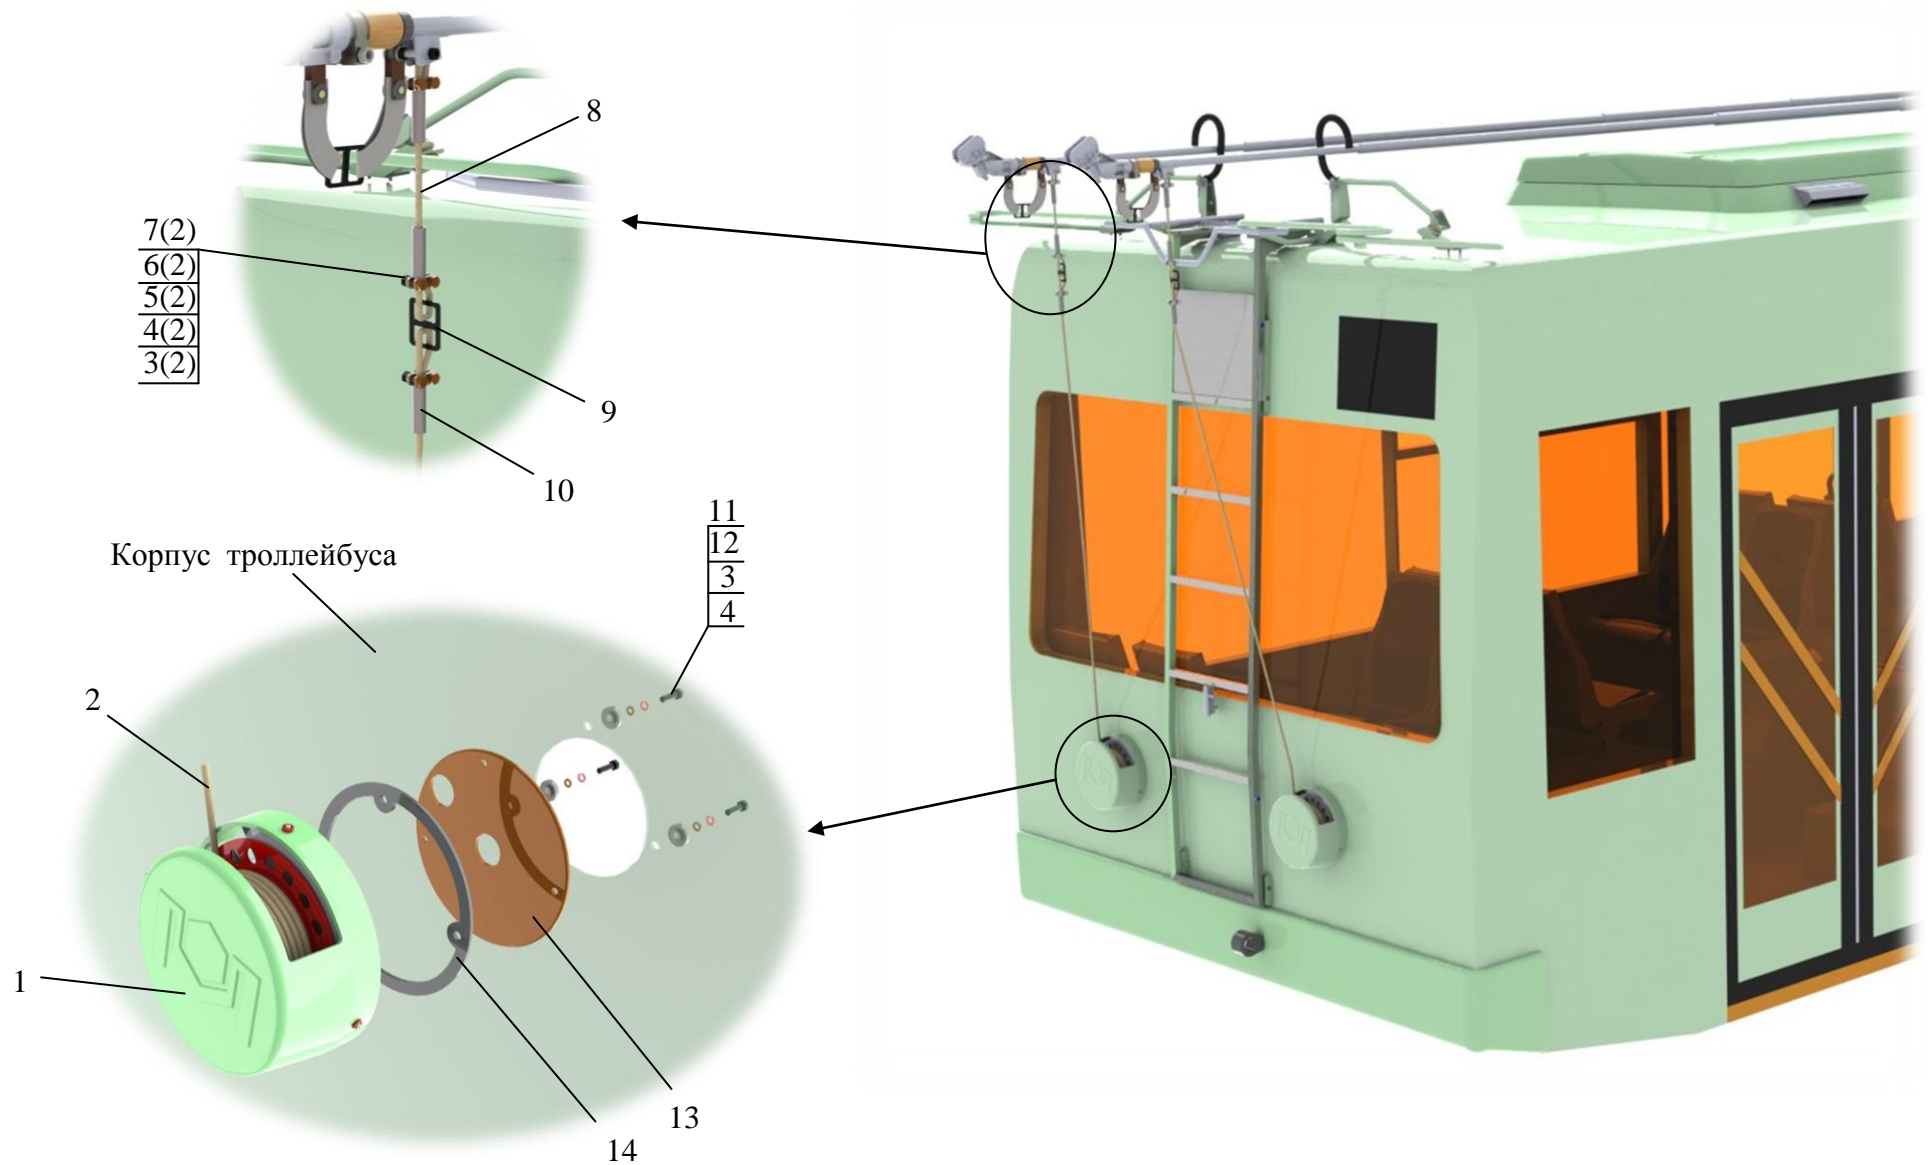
Установка механизмов укладки шнура АКСМ 321-360300.000
